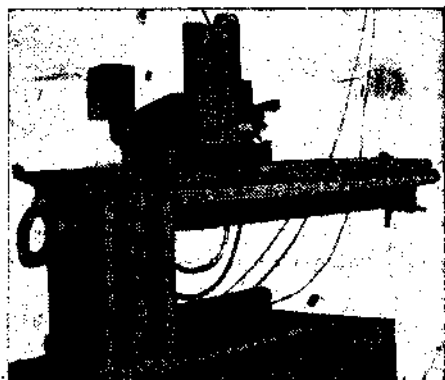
Автомат для сварки продольных швов цилиндрических предметов.
